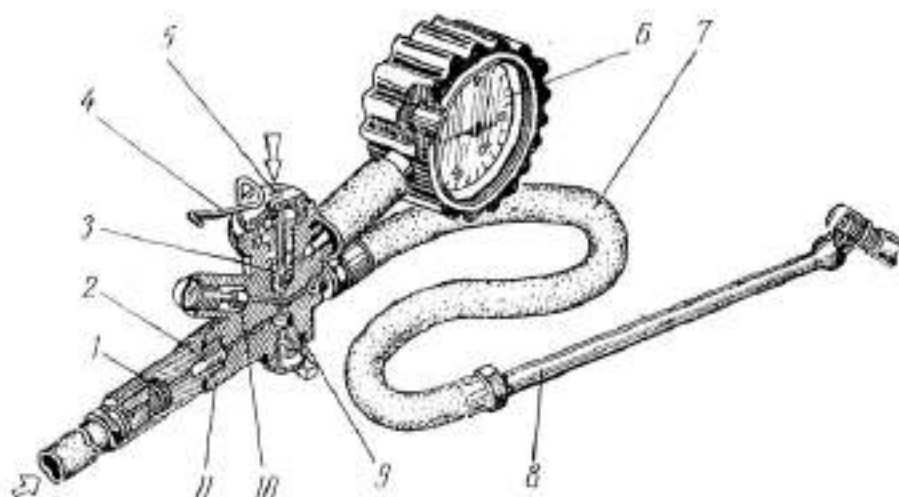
Наконечник с манометром для воздуховоздухораздаточного шланга:
